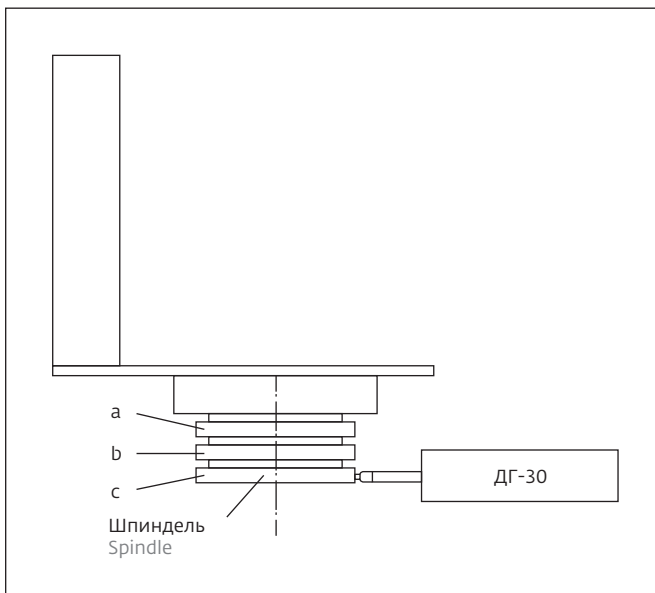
Крепление шпинделя при поверке. На роторе шпинделя показаны дорожки a, b и c
